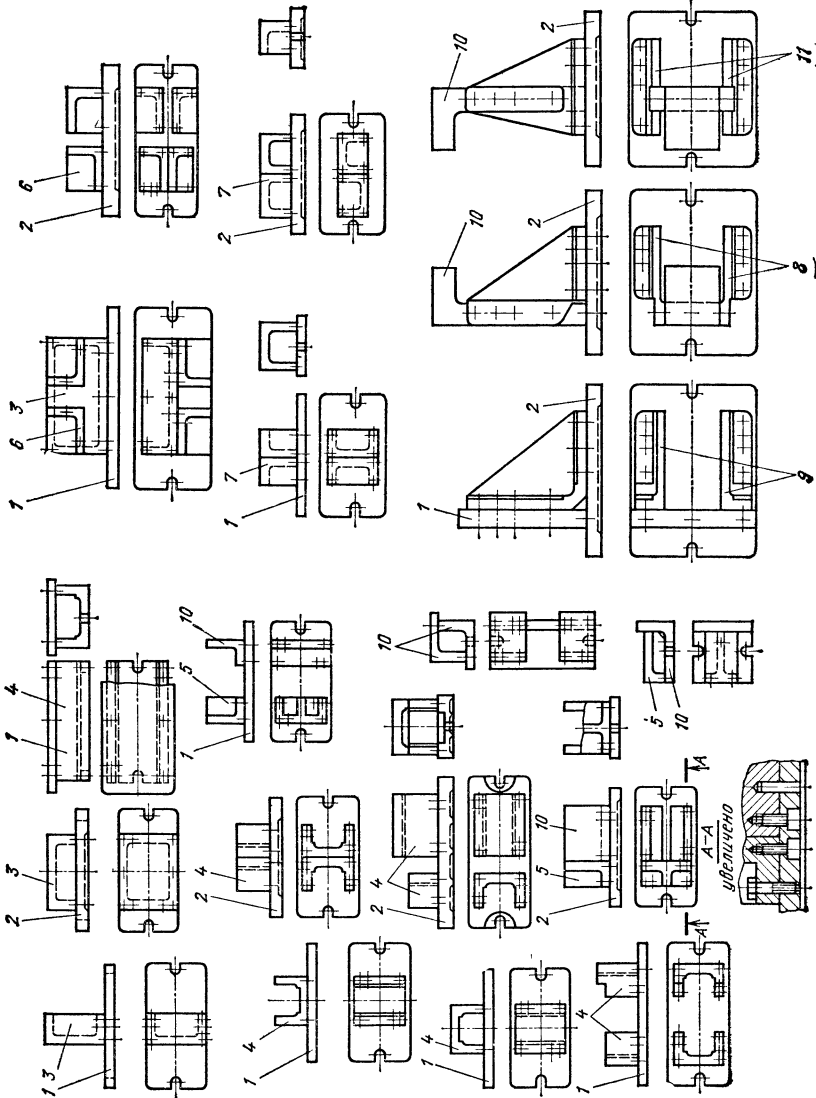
Примеры компоновки корпусов из стандартных элементов:
